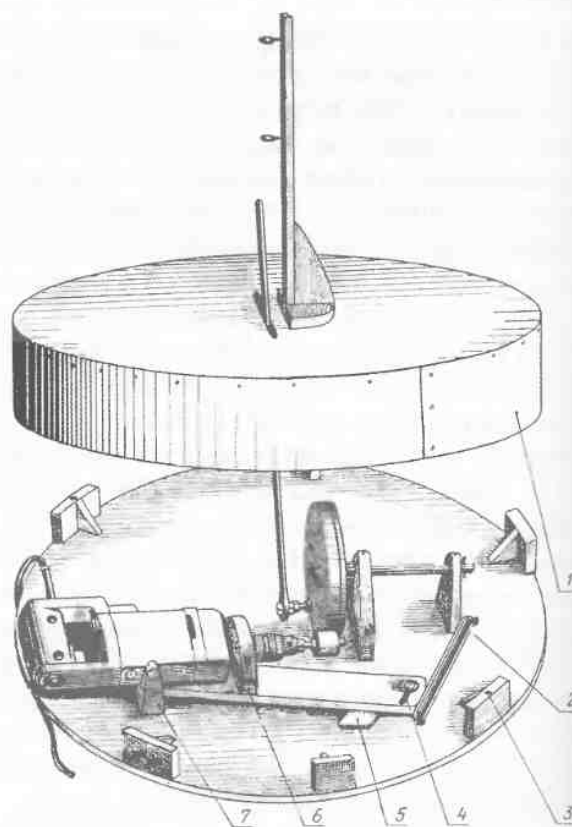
Внутреннее устройство кожуха механического лобзика: 1 — войлочная обложка крышки кожуха; 2 — резиновый шнур прижатия ролика к колесу; 3 — фиксирующее отверстие для направляющего штифта крышки; 4 — прорезь под шуруп для поворота основания дрели; 5 — войлочная подкладка; 6 — деревянный зажим шейки дрели; 7 — деревянное гнездо корпуса дрели
